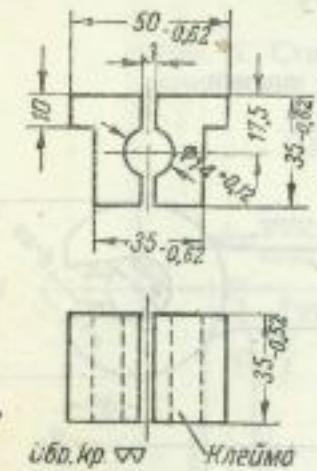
Приспособление для обжатия прицельного хомуттика Д-ПП ПМ-21.
